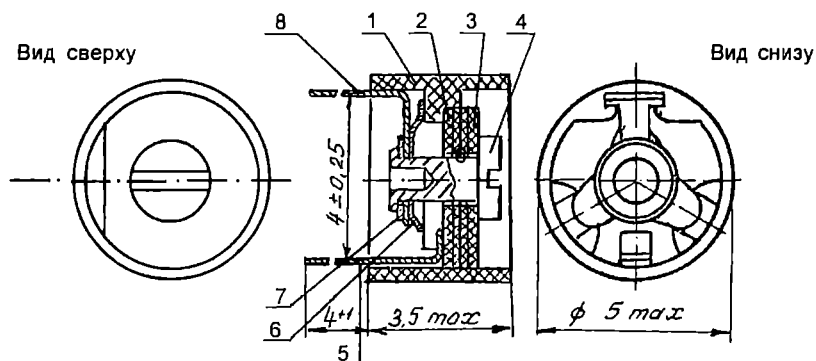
Схема конструкции конденсатора КТ4-25. 1 - корпус, 2 - статор, 3 - ротор, 4 - ось, 5 - статорный вывод, 6 - пружина, 7 - прижимная шайба, 8 - роторный вывод
